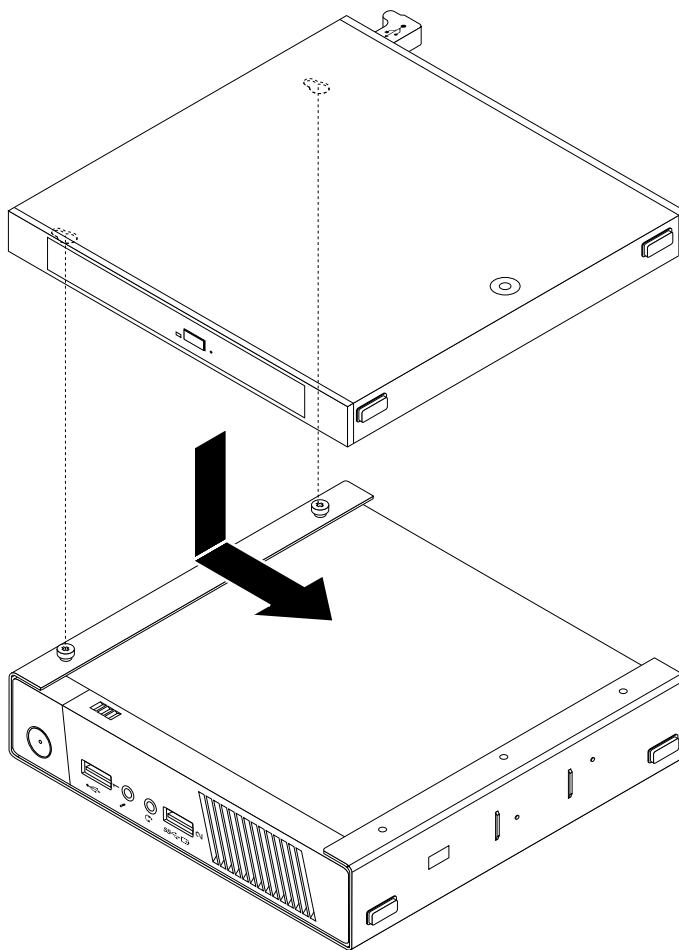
Установка корпуса внешнего дисковод для оптических дисков
